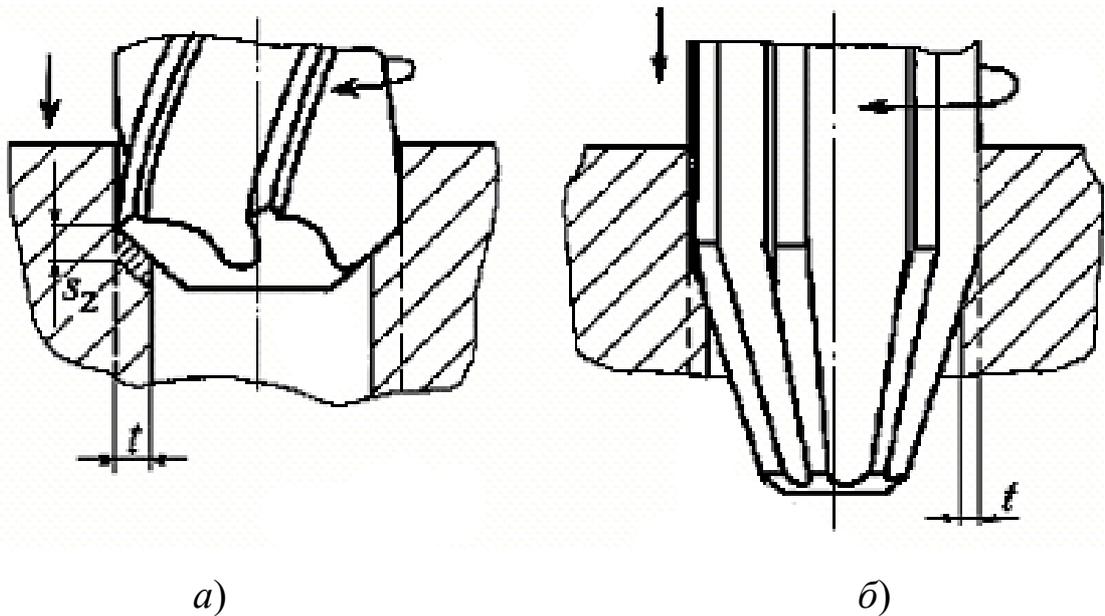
Обработка поверхности: а) зенкером, б) – разверткой
